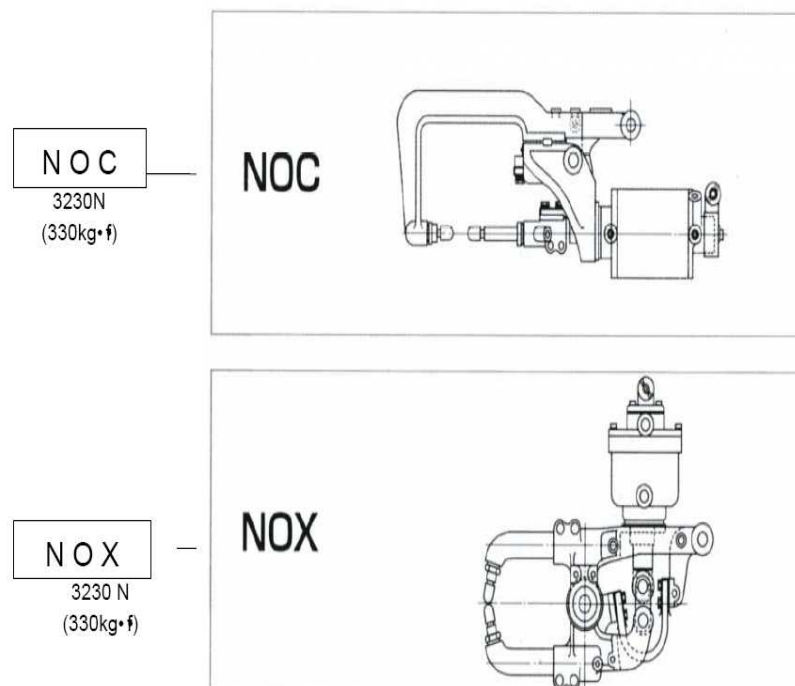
Soldadoras de Punto Móviles en C y en X
